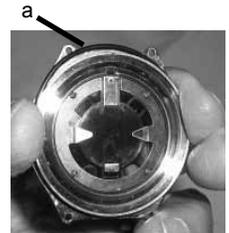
COMPRESIONE DELL'O-RING DEL COPERCHIO
